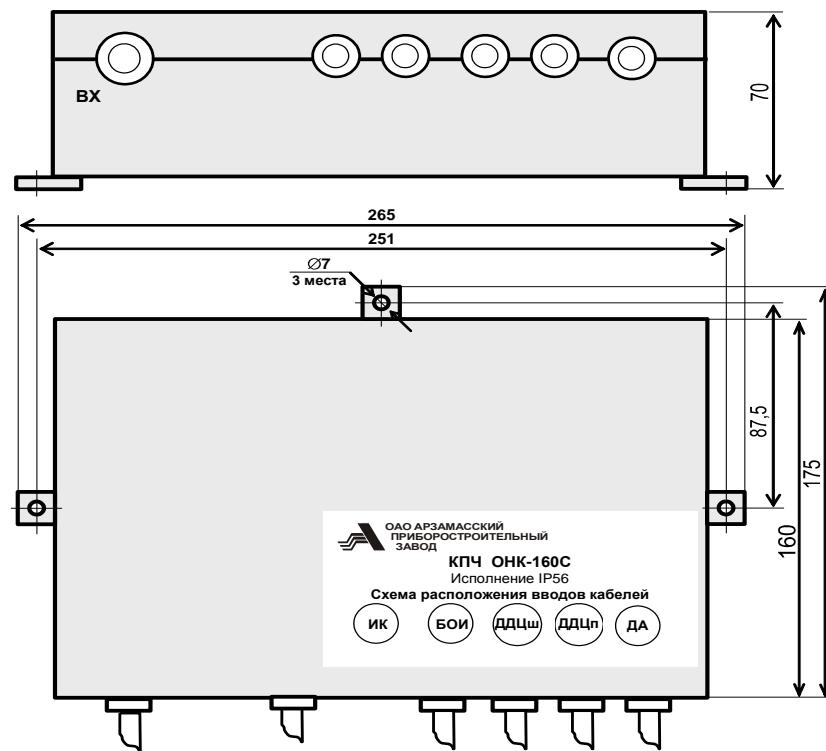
Габаритные и присоединительные размеры КПЧ
